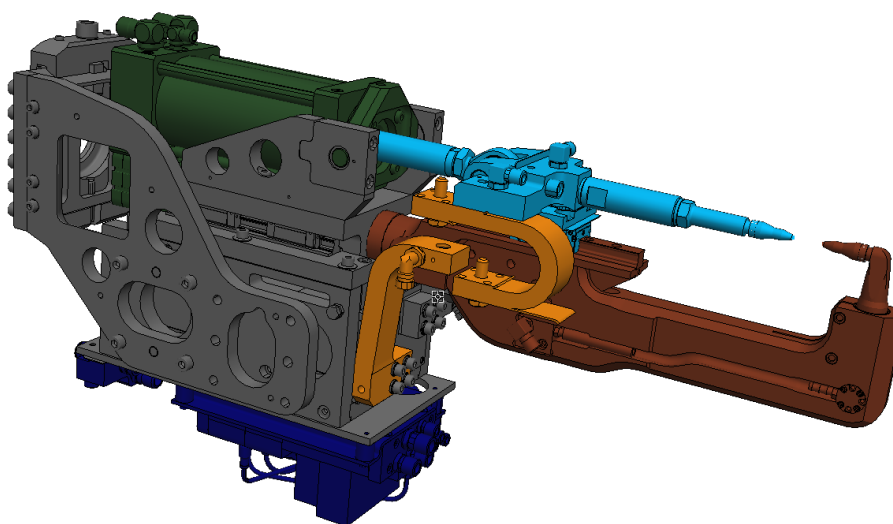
Сварочный пистолет для стационарной сварки
